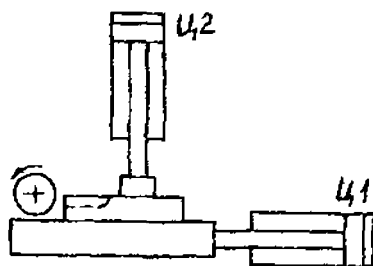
Конструктивная схема подачи стола фрезерного станка
